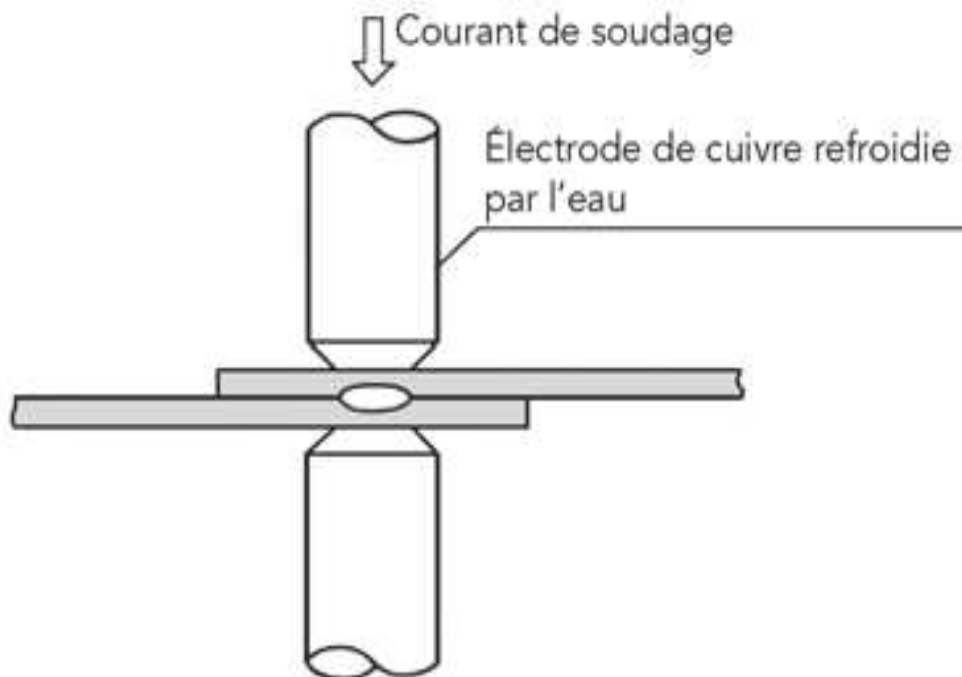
Principe du soudage électrique par résistance par points [2].
